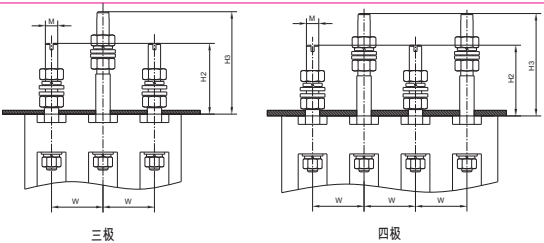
NXMLE-125、160、250、320板后接线外形及安装尺寸
